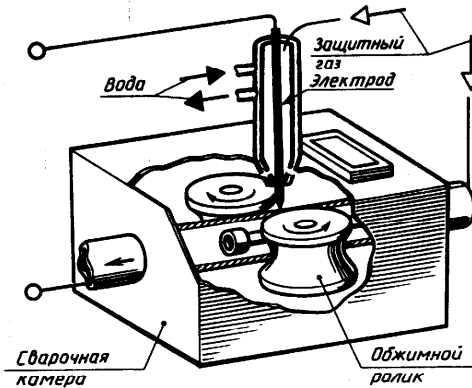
Схема сварки трубы в контролируемой атмосфере
